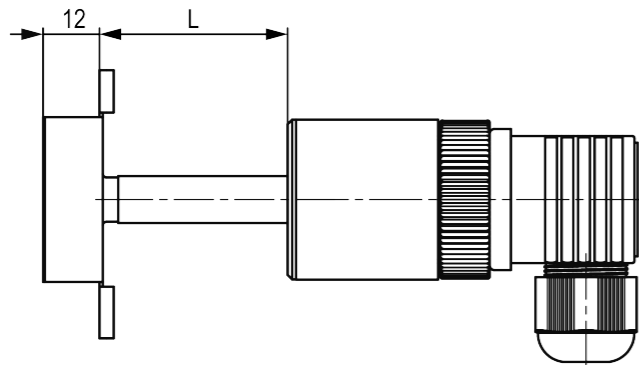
Габаритные и установочные размеры модели ДТС3222.И
